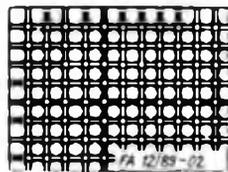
Ausschnitt aus dem Layout der Universalleiterplatte
